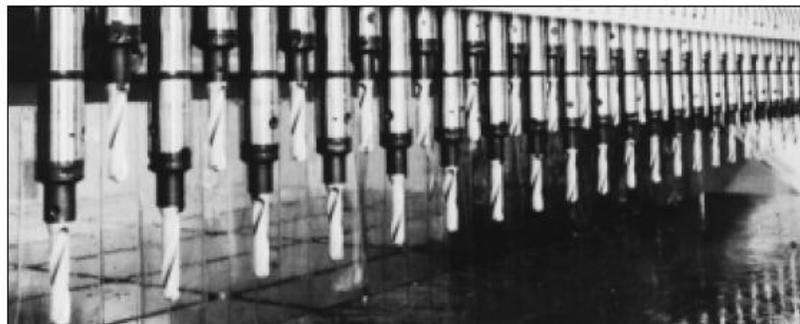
Mesin Gurdi (*Drilling Machine*)
